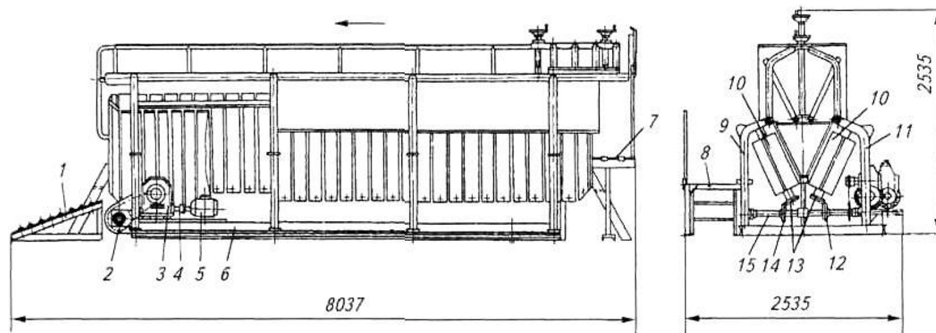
Фіксувальний V-подібний конвеєр Г2-ФПКФ для глушення свиней :
